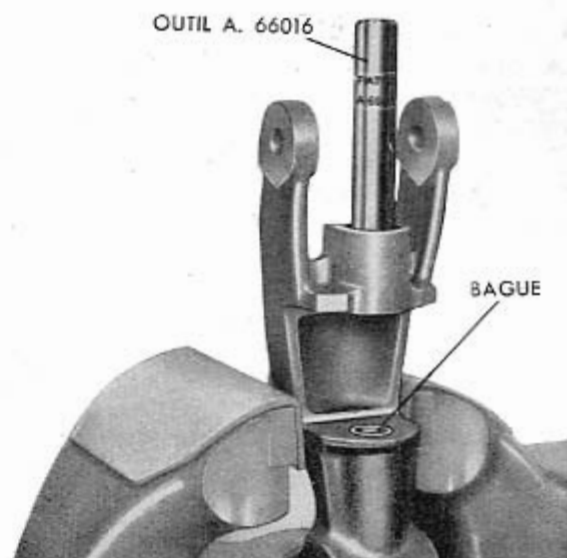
Outil A. 66016 pour démonter et monter sur le montant les bagues du pivot de fusée.
